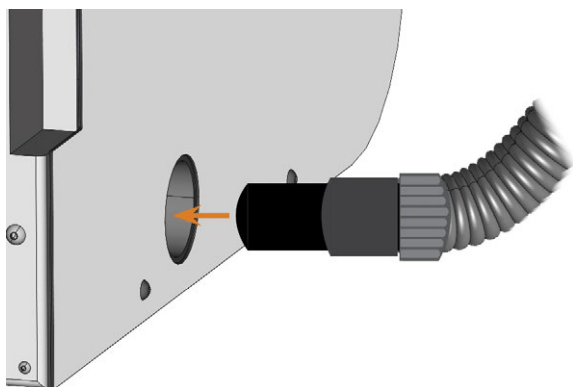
INSERIMENTO DELLA CONNESSIONE DEL TUBO NELL'APERTURA DEL SISTEMA DI ESTRAZIONE DELL'ARIA
